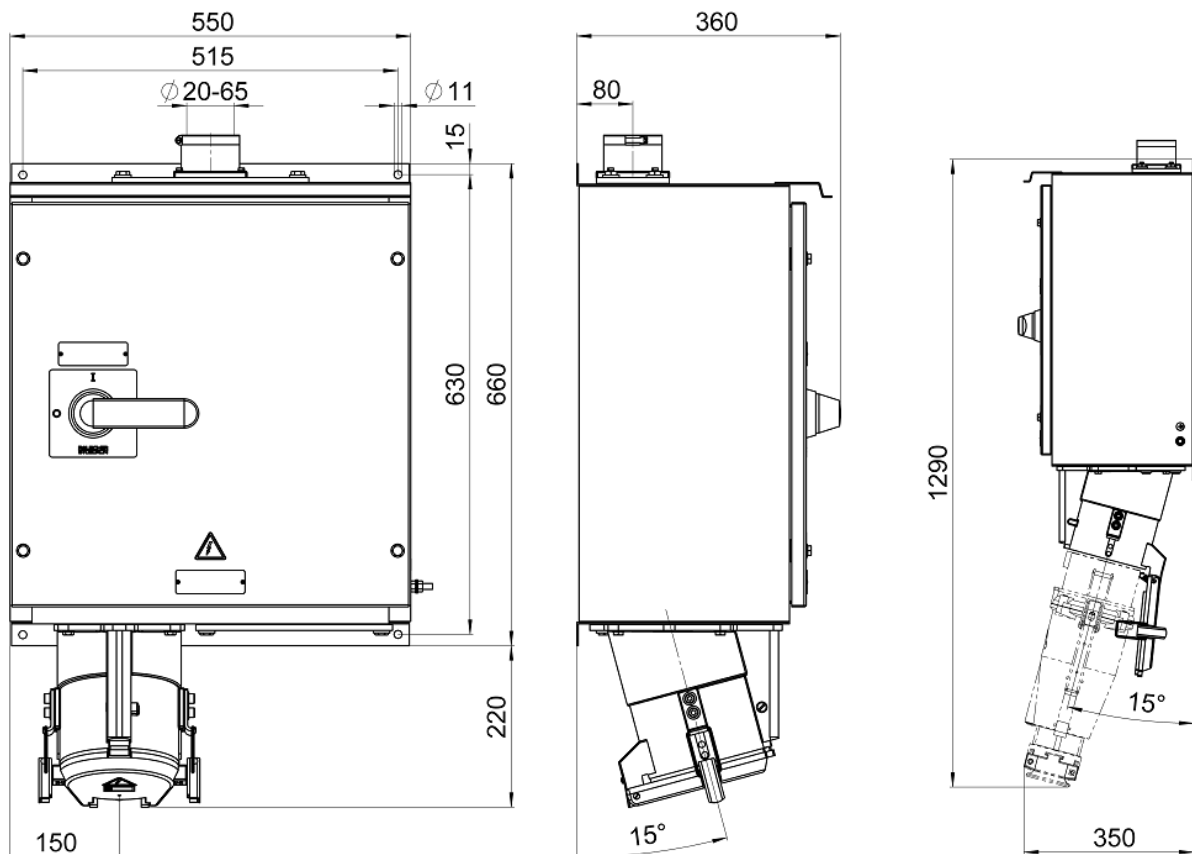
Abmessungen Anschlusskasten mechanisch verriegelt CUMI 250 A und 400 A in mm
